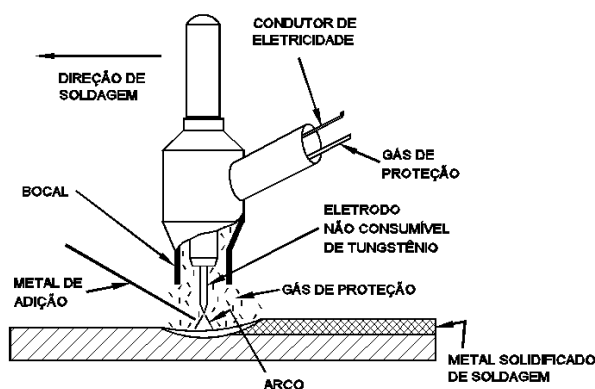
Soldagem TIG (esquemática) <sup>[2]</sup>
